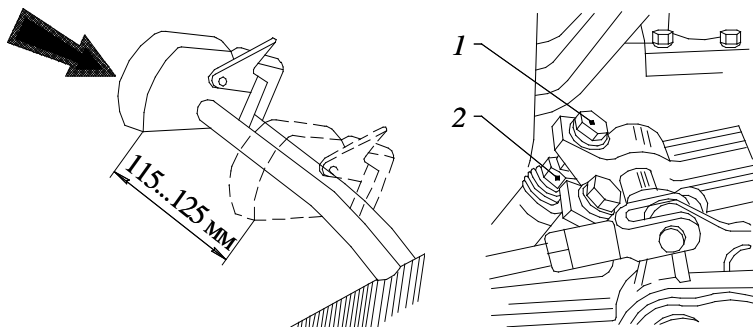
Схема проверки и регулировки рабочих тормозов:
